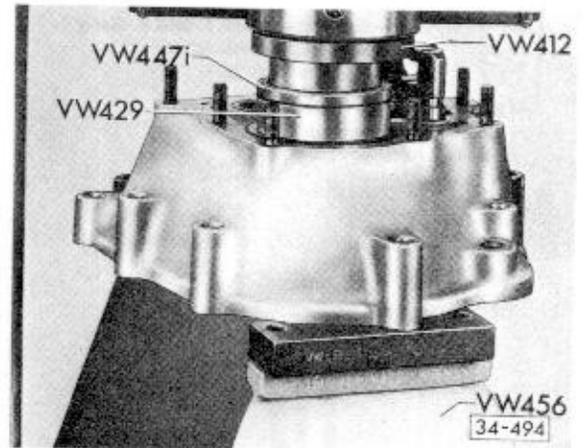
Rillenkugellager für Antriebswelle einpressen
